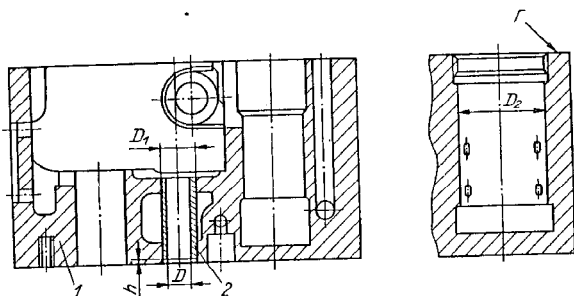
Корпус 1 средний в сборе /рис. 129/
